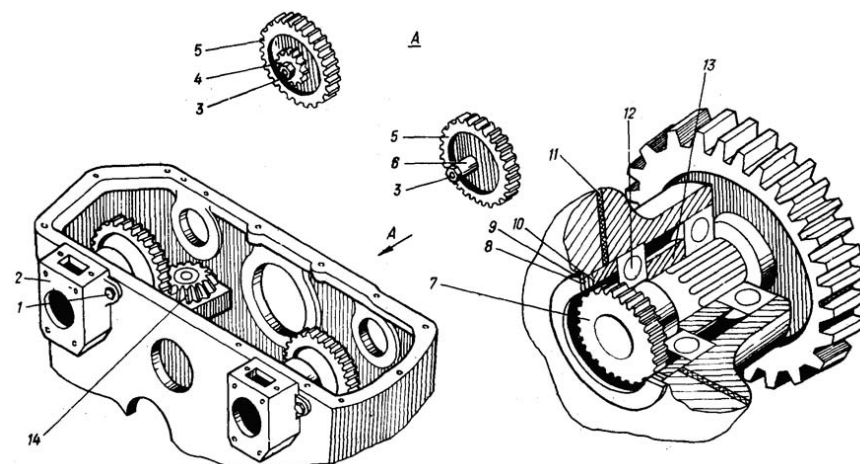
Снятие колес зубчатых привода насосов: 1 — болт; 2 — корпус; 3 — гайка; 4, 5, 14 — колеса зубчатые; 6, 10, 13 — втулка; 7 — вал; 8, 9 — шайба; 11 — прокладка; 12 — подшипник
